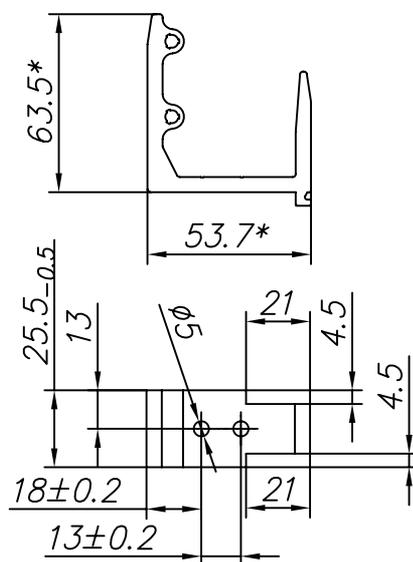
Изготовление соединителя FLGU.400.0913
